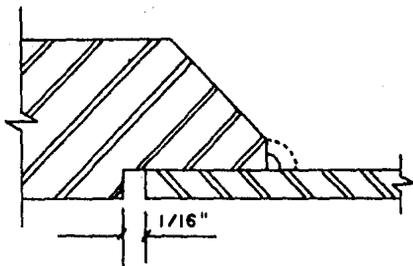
ESPACIAMIENTO PARA EFECTUAR UNA SOLDADURA DE INSERTO SOLDABLE
